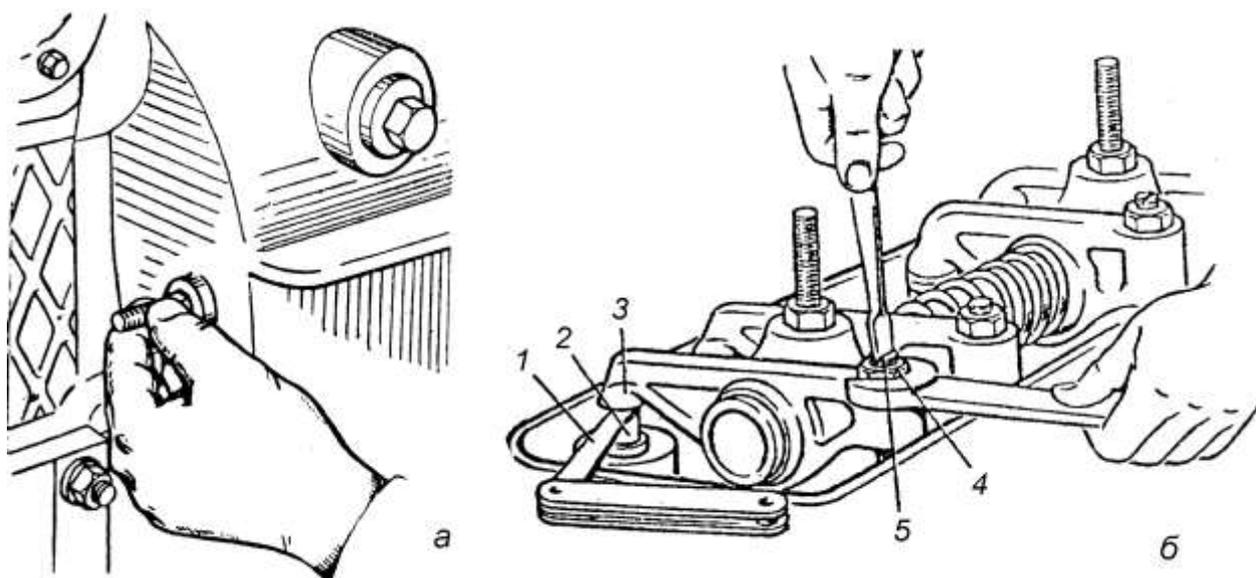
Проверка и регулировка теплового зазора в клапанном механизме:
